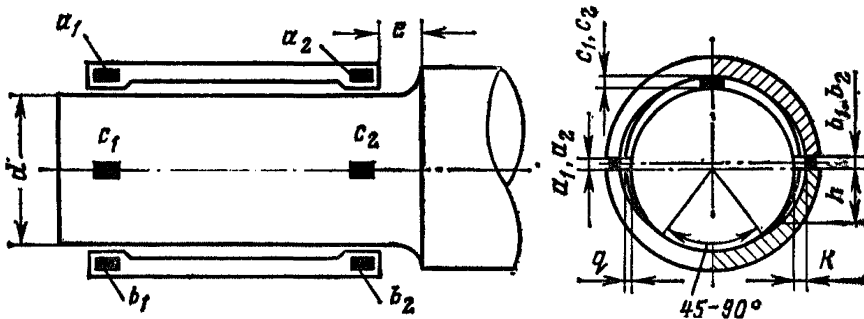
Измерение зазоров в подшипниках скольжения
